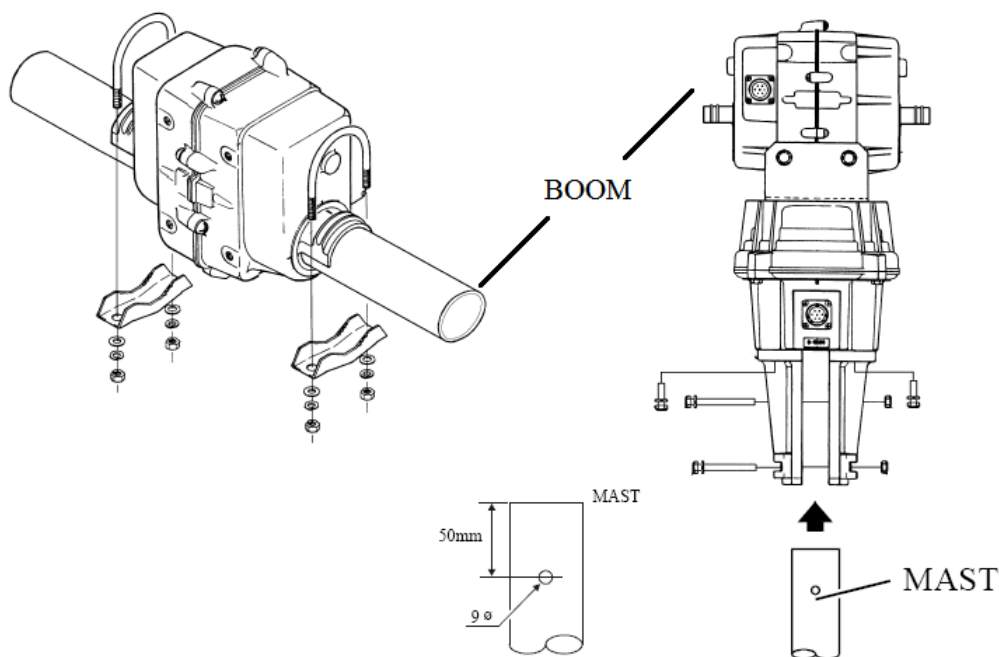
Montagem e instalação do Rotor G-5500 da YAESU
